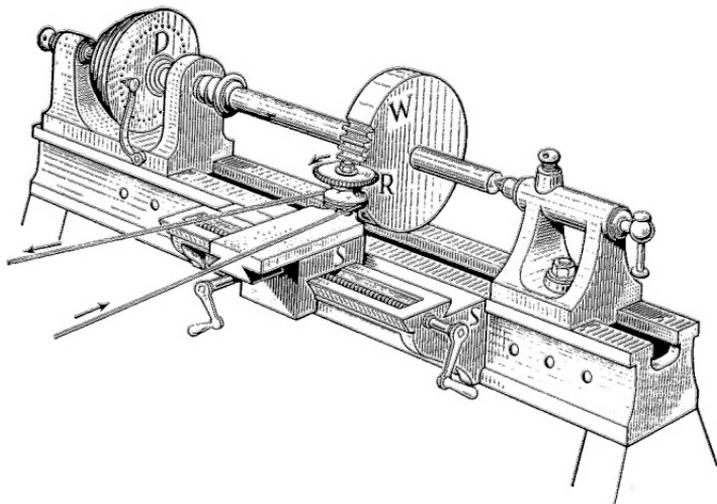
Принцип устройства токарно-винторезного станка, 1841 г. Рисунок Джеймса Несмита
